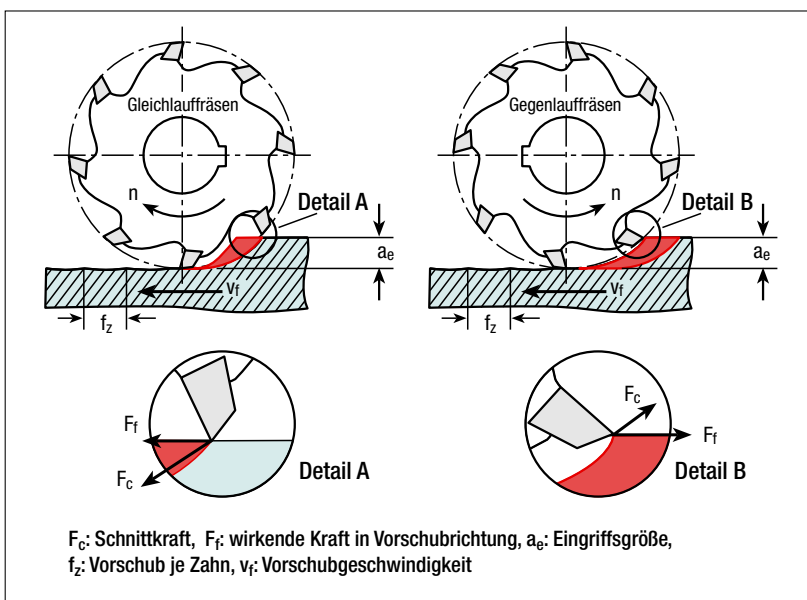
Umfangsfräsen im Gleich- und Gegenlauf
